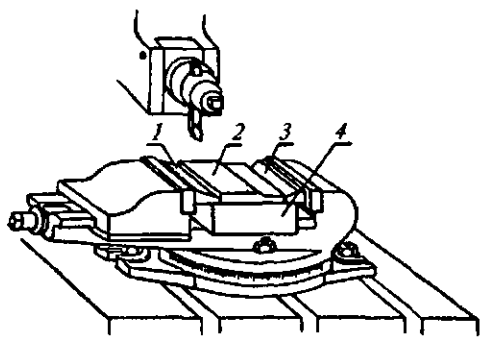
Схема установки и закрепления тонких деталей в машинных тисках
